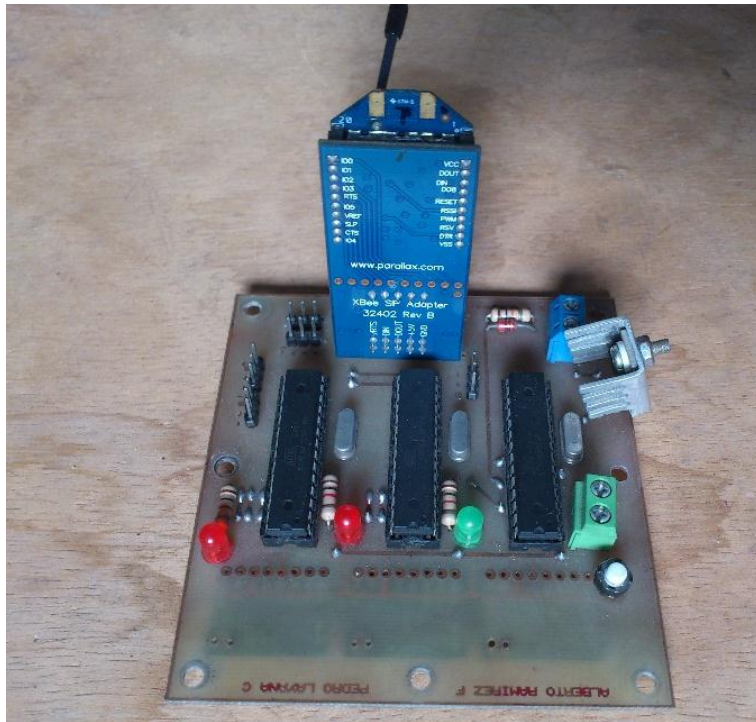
Vista Frontal de placa controladora. Placa controladora construida en el proyecto.
